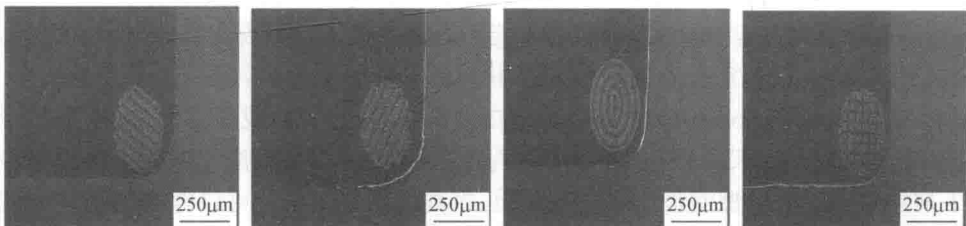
硬质合金刀具表面纳秒激光加工的微织构形貌
